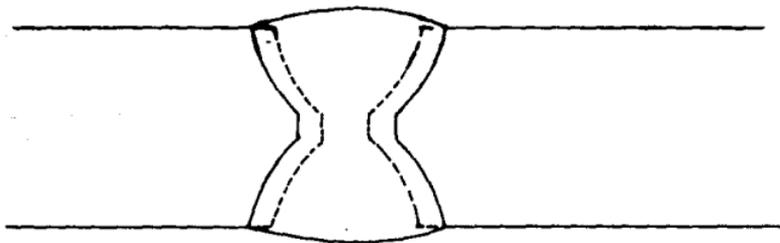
Soldadura con Bisel Doble en U
